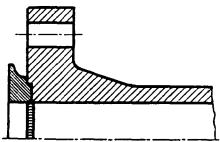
Stahlgußflansch mit eingesetztem Ansatz und Schweißlippe.
